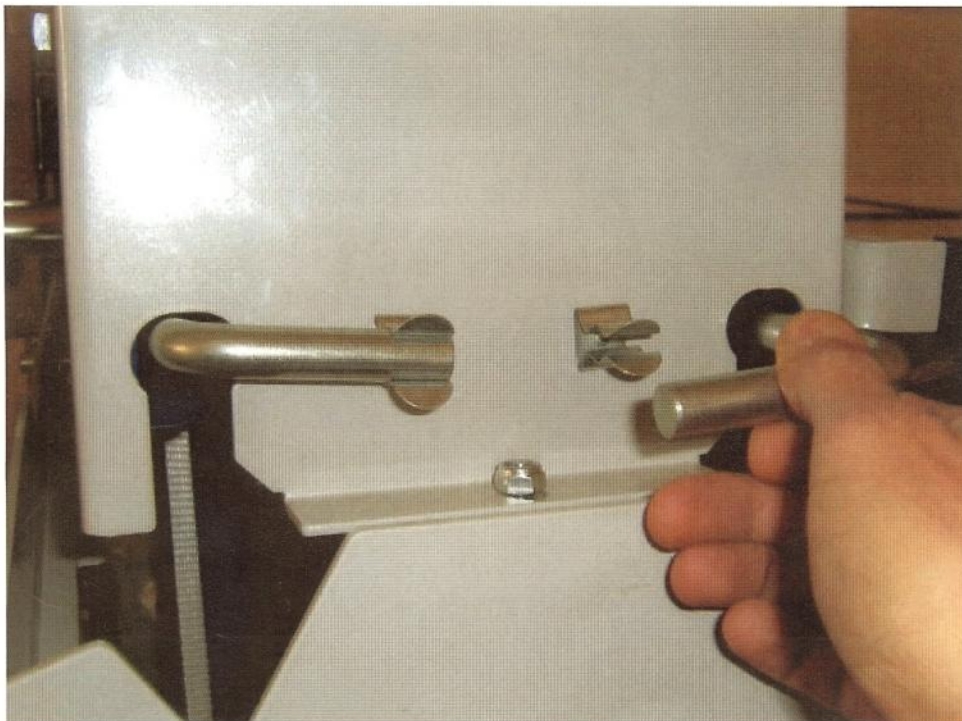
Anschließend den Zylinder mit den Fixierbolzen befestigen
